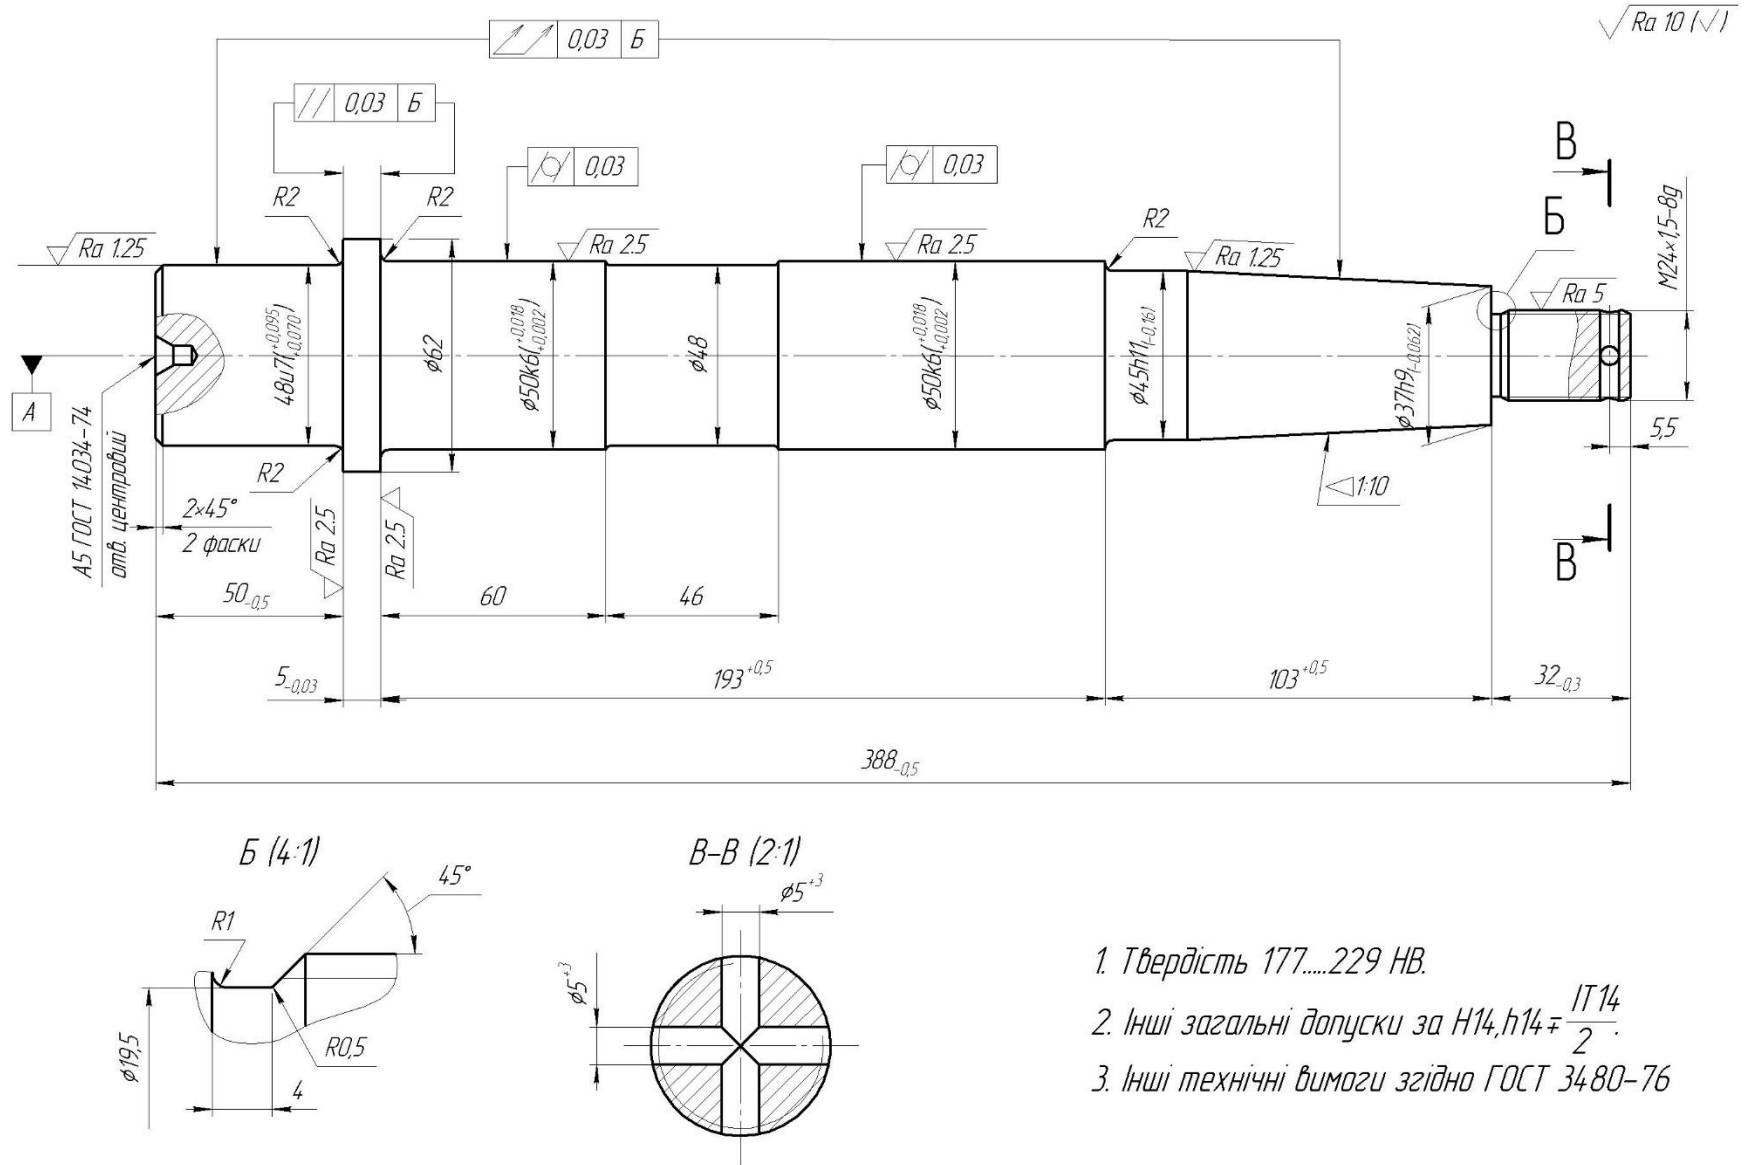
Кресленик деталі «Вал ступінчастий»
